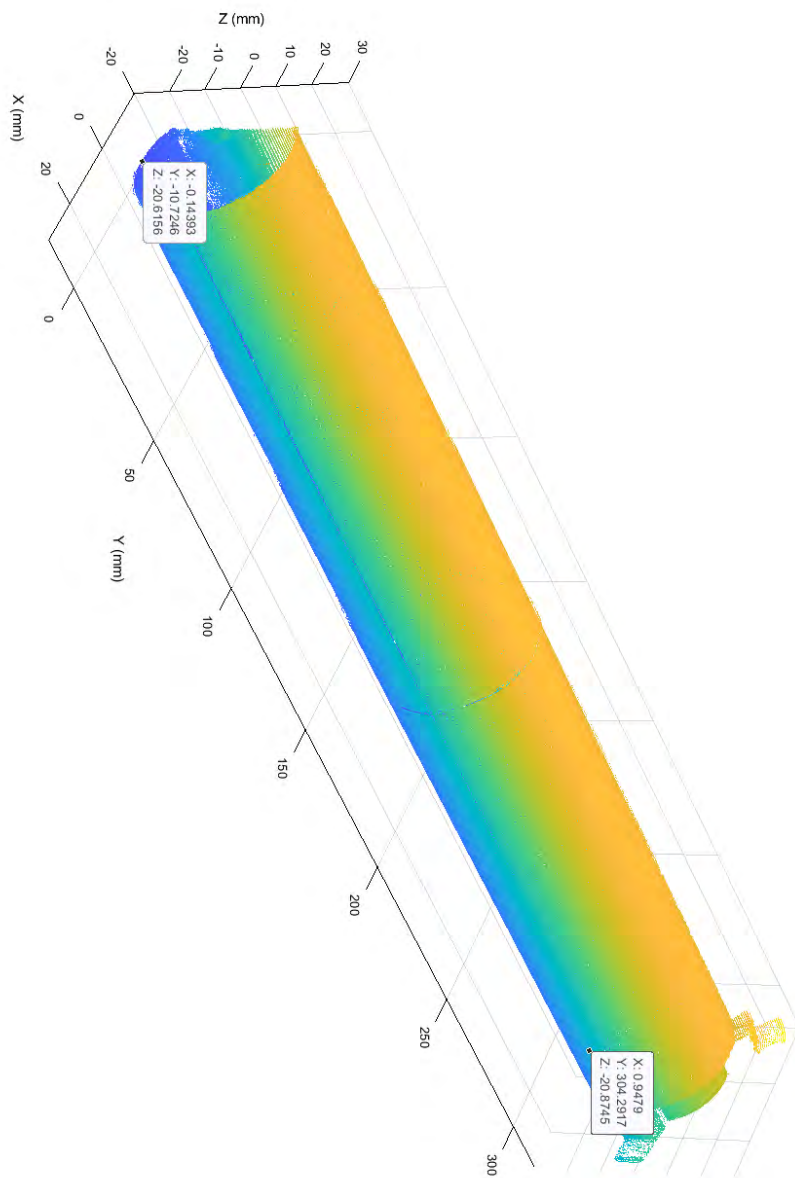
Medida en el eje Y de la primera reconstrucción del cilindro de ajuste del plano láser
